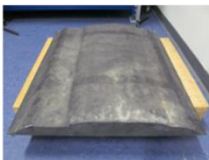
CFK-Halbzeuge für Hardpatch-Werkzeuge
